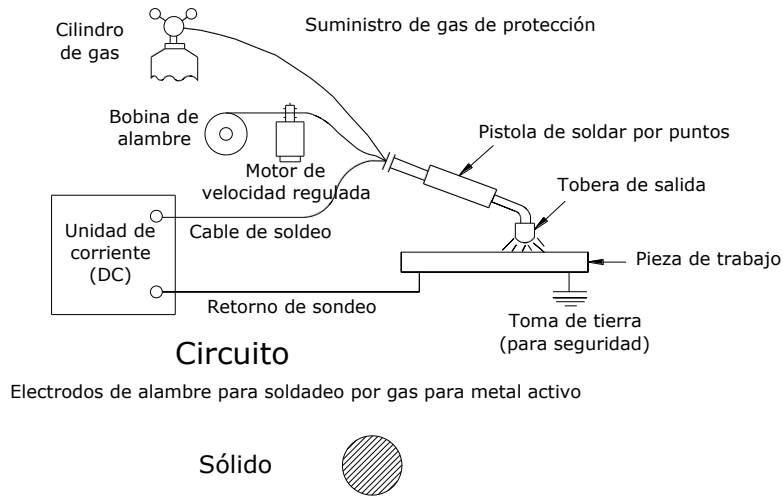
Proceso de soldadura GMAW (soldadura de metal con gas inerte).
